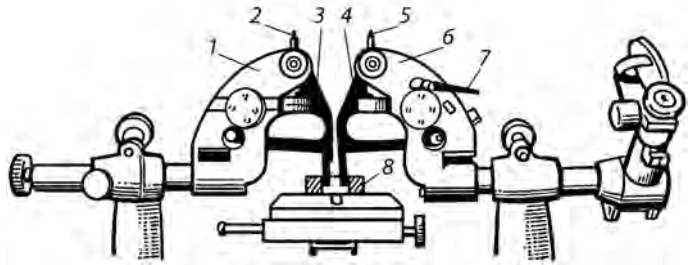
Пристрій для вимірювання внутрішніх розмірів:
